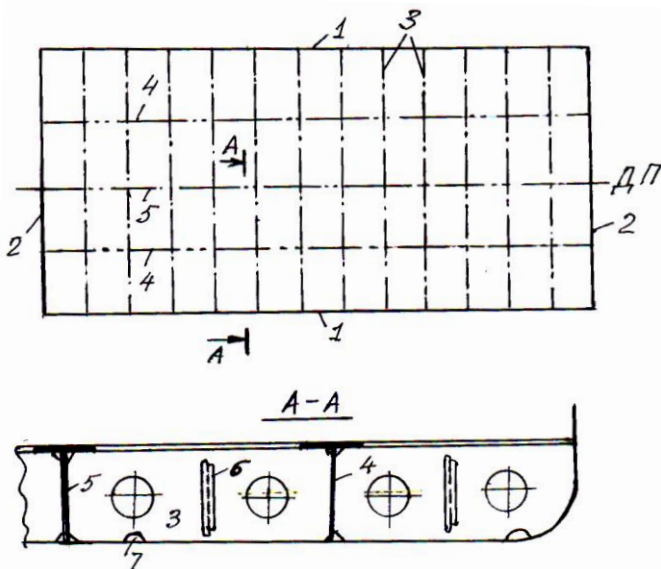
Схема днищевого перекрытия при поперечной системе набора:
